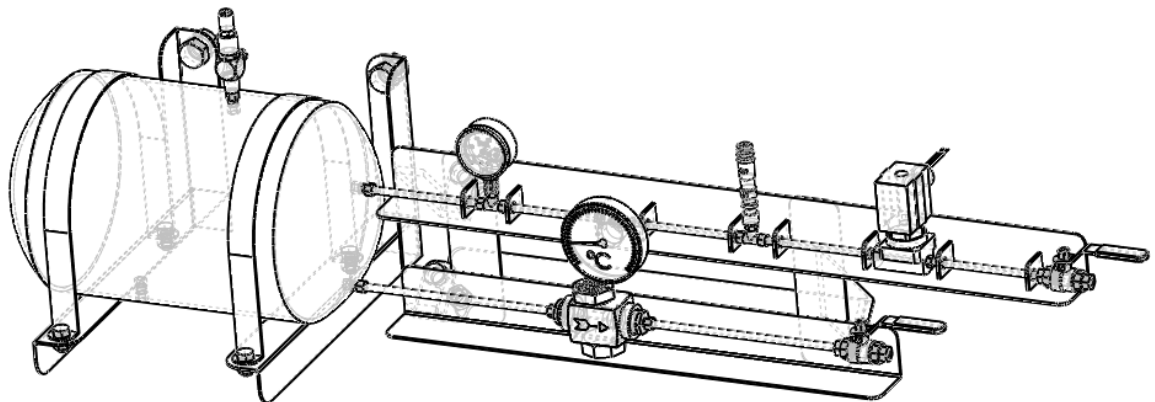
Válvulas y sensor del sistema de entrada. De izquierda a derecha, válvula tipo check, de globo, de diafragma y un sensor de presión digital.
